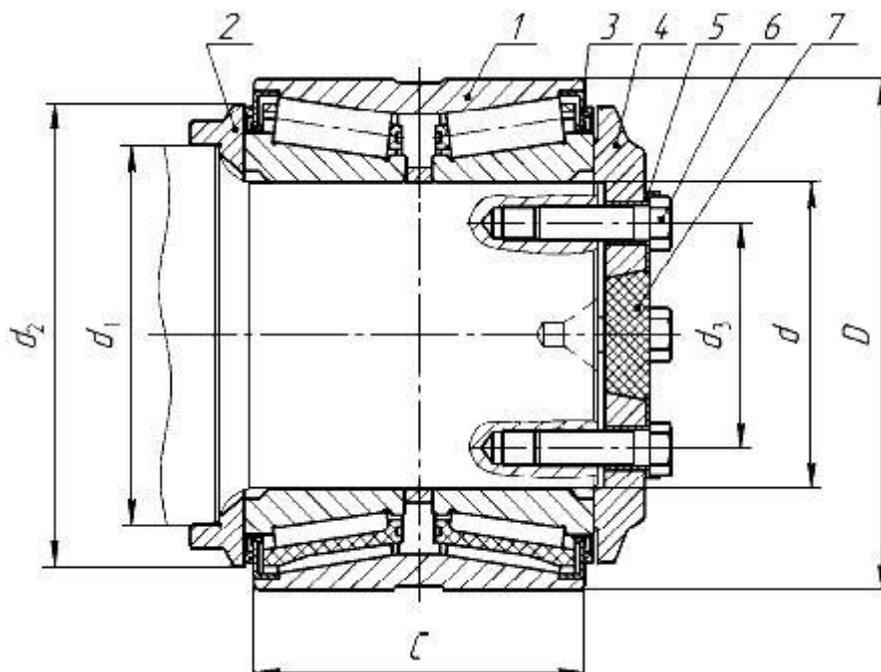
Конструктивное исполнение конического подшипникового узла с передней крышкой с четырьмя болтами и с заглушкой
